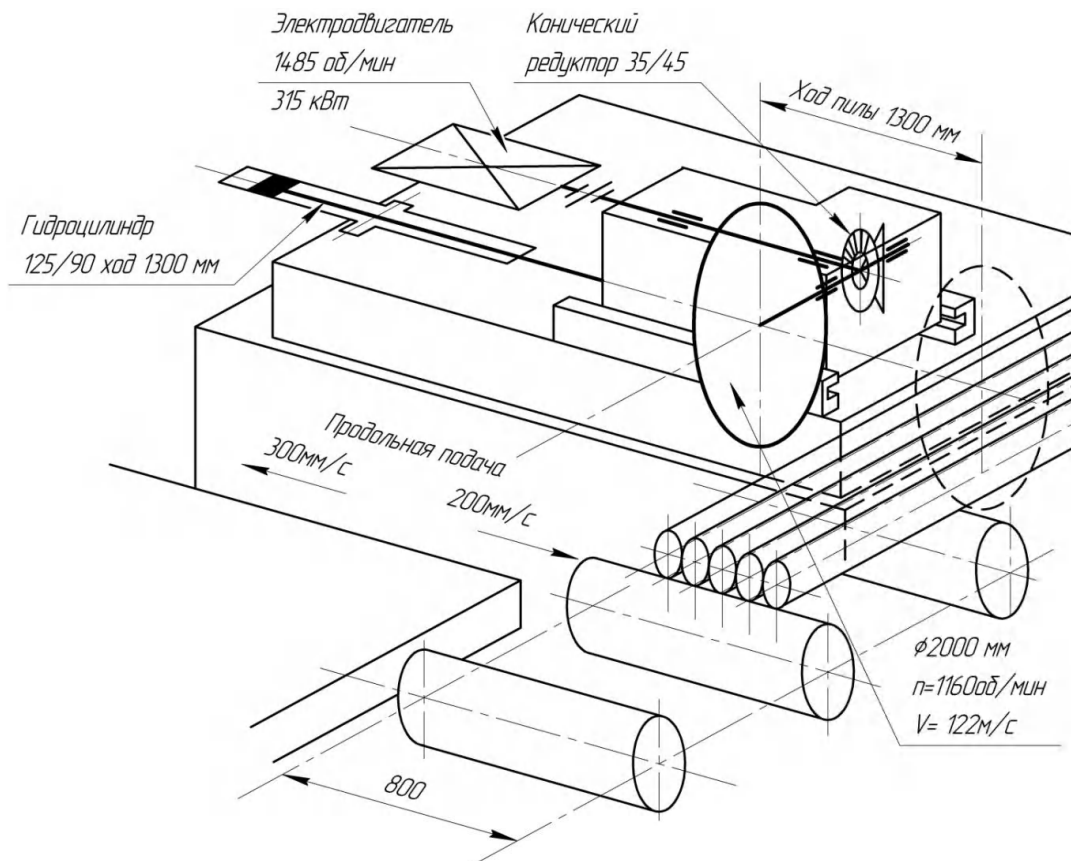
Кинематическая схема салазковой пилы пакетной резки
